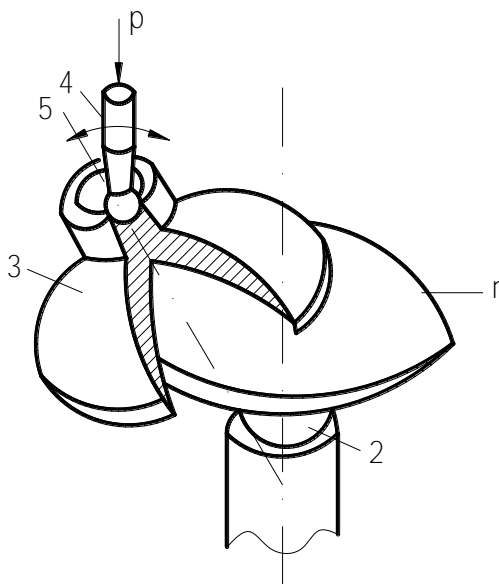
Схема формообразования сферической поверхности заготовки способом свободного притира
